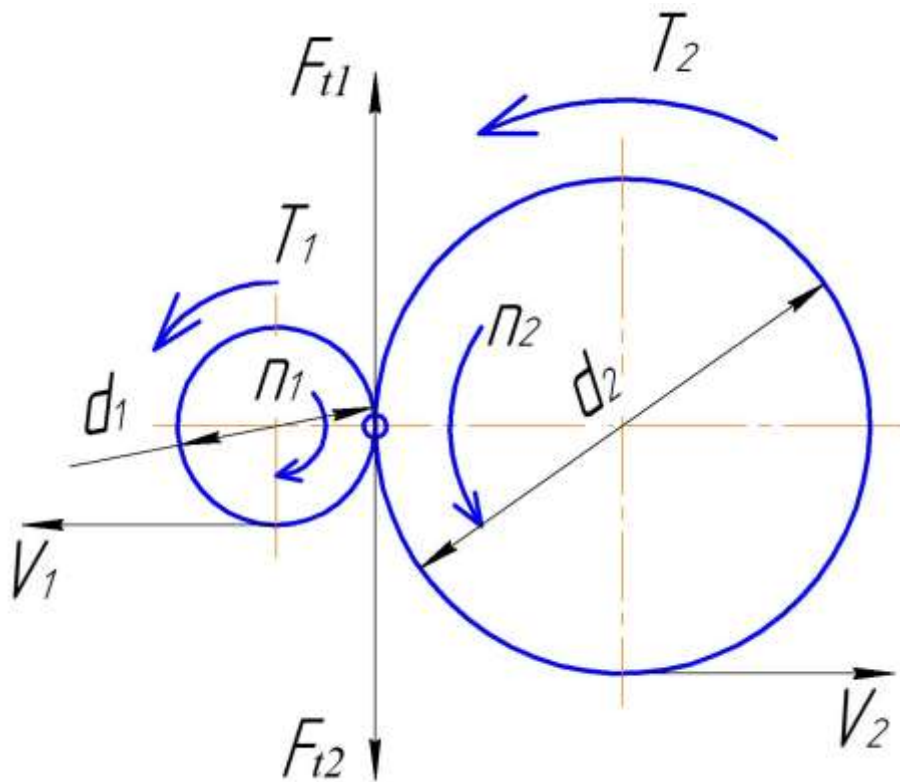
Розрахункова схема передачі обертового руху
